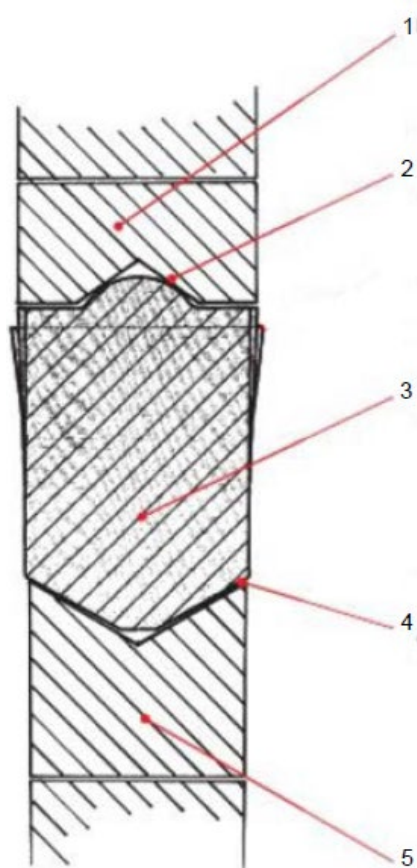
Схема кріплення державки з пластиною в розрізі
